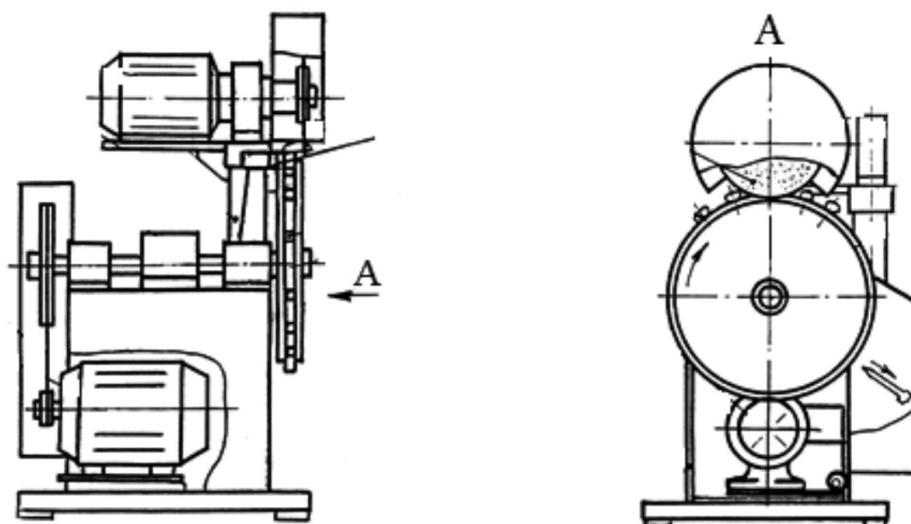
Отрезной станок с непрерывной подачей заготовок
